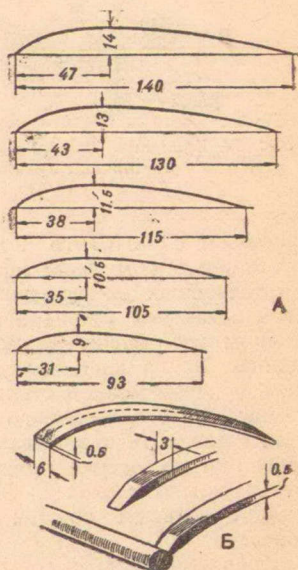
Нервюры крыла: А — чертеж нервюр, Б — заготовка для нервюр и способ соединения нервюр и кромки.
